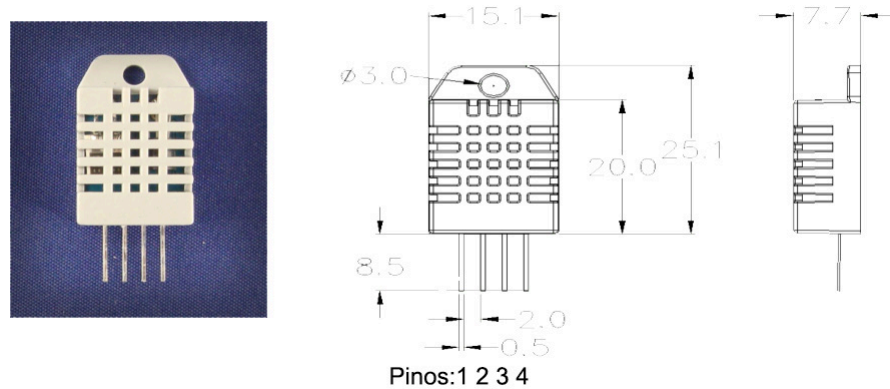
Sensor DHT22 e dimensões em milímetros [10].
